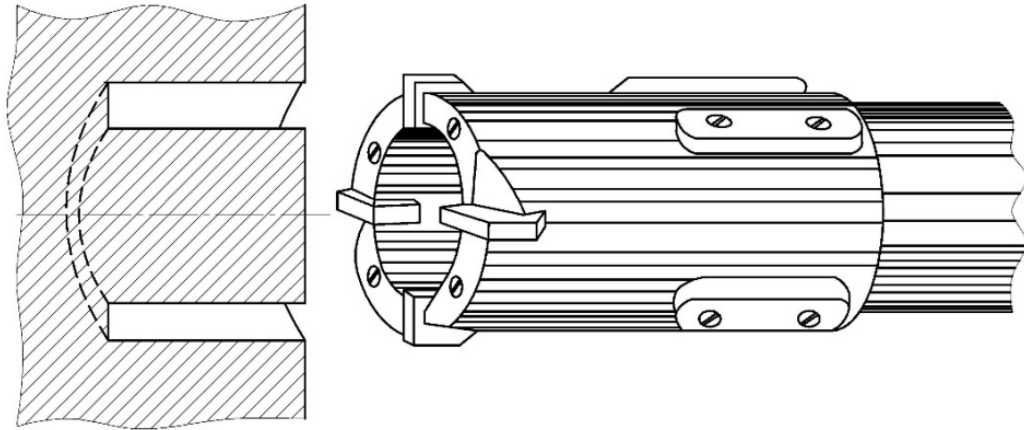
Схема оброблення свердлом для кільцевого свердління
